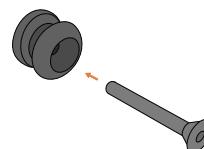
Einsetzen der Senkkopfschraube in die Schlaufenverbindung.
